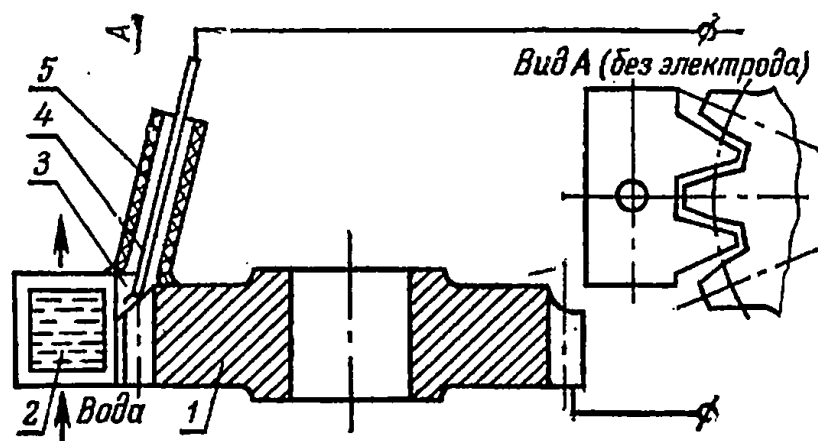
Схема наплавки изношенных торцевых поверхностей зубьев шестерен:
